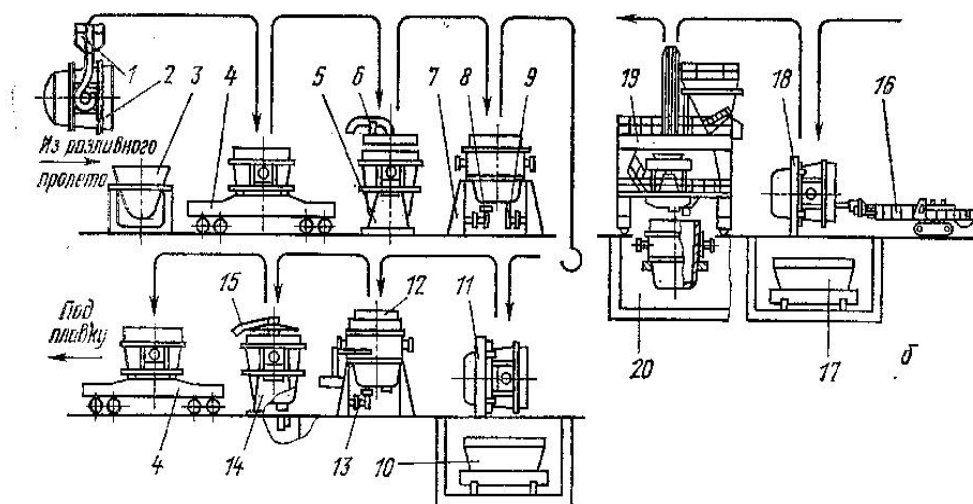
Схема межплавочной подготовки и ремонта футеровки сталеразливочных ковшей: 1 — траверса мостового крана; 2 — ковш; 3 — шлаковый ковш; 4 — сталевоз с ковшом; 5, 7, 14 — стенд; 6 — охлаждение футеровки ковша; 8 — манипулятор для снятия и установки шиберных затворов; 9 — шиберный затвор; 10, 17 — короб; 11, 18 — стенд поворотный; 12 — кесон для установки стаканов; 13 — шиберный затвор; 15 — устройство для нагрева футеровки ковша; 16 — машина для ломки футеровки; 19 — устройство для набивки футеровки ковша; 20 — яма для кладки новой футеровки ковшей
